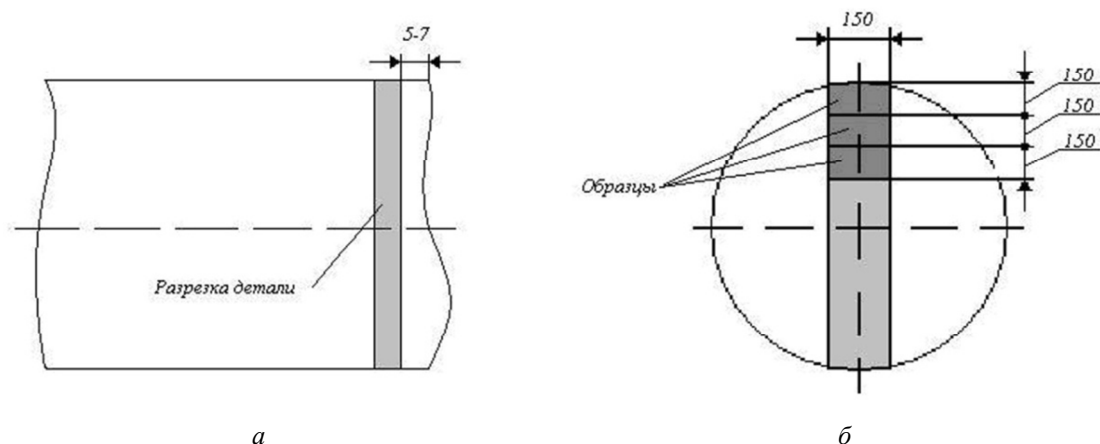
Схема изготовления образцов в зоне разрушения гребного вала:
